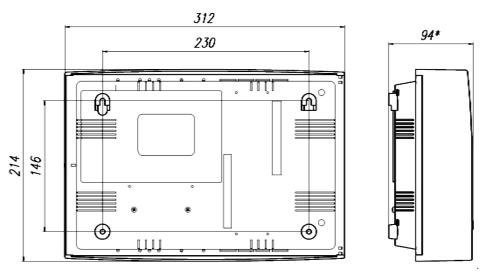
Габаритные и установочные размеры прибора Vita 02M.
